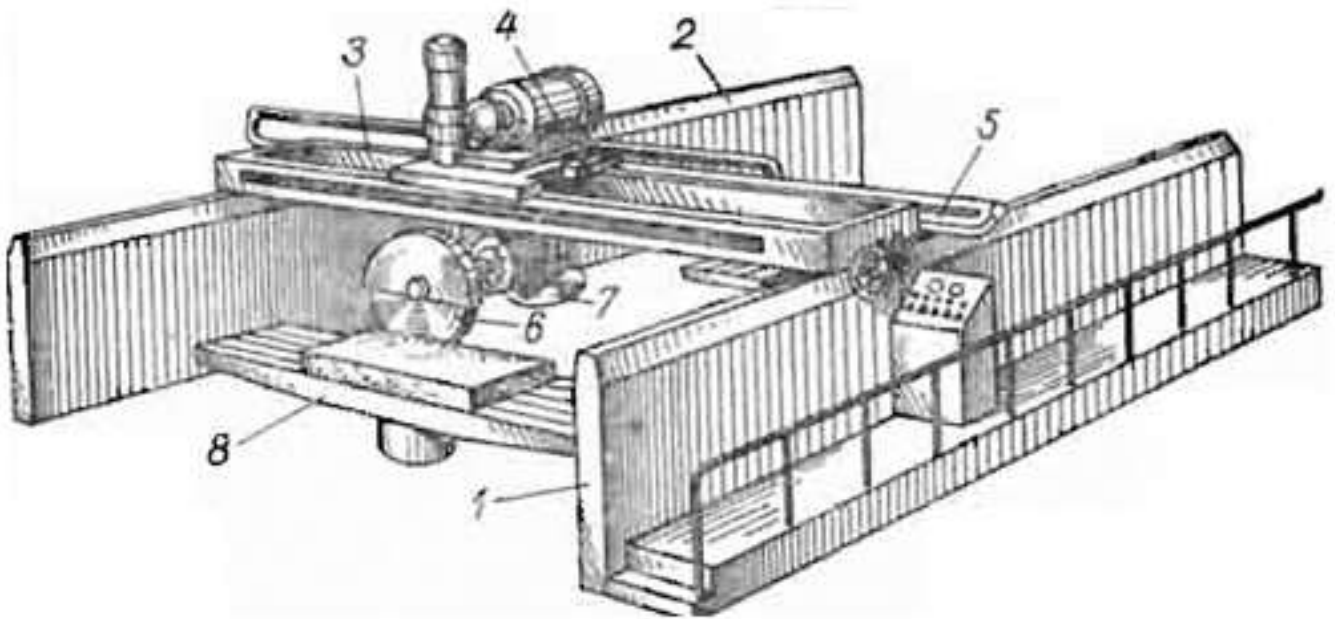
Окантовочно-фрезерний мостовий верстат СМР-015 [3]: загальний вигляд;
